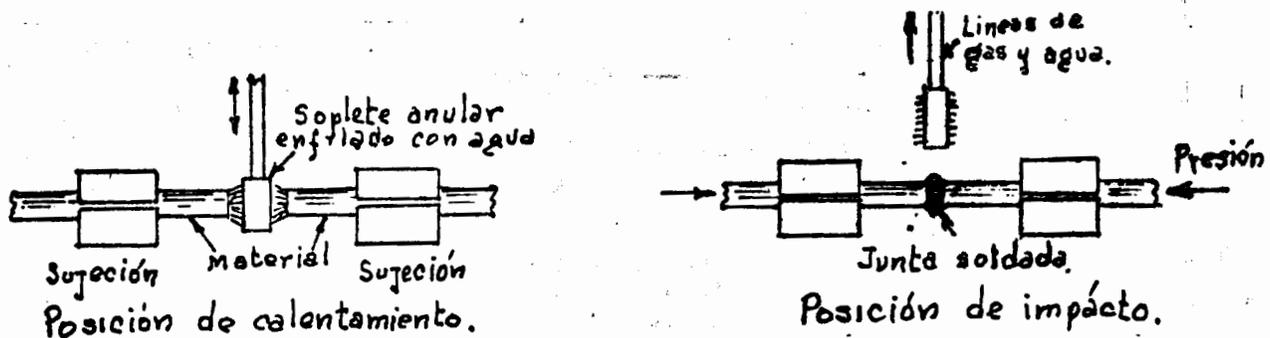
ESQUEMA DE UNA SOLDADURA A PRESION CON GAS.
